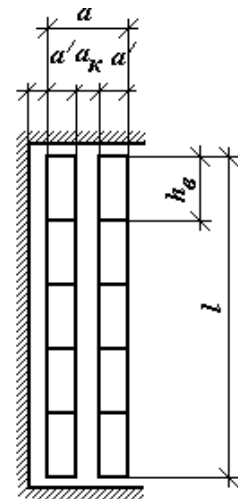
Размеры двухслойной цилиндрической обмотки с осевым каналом
